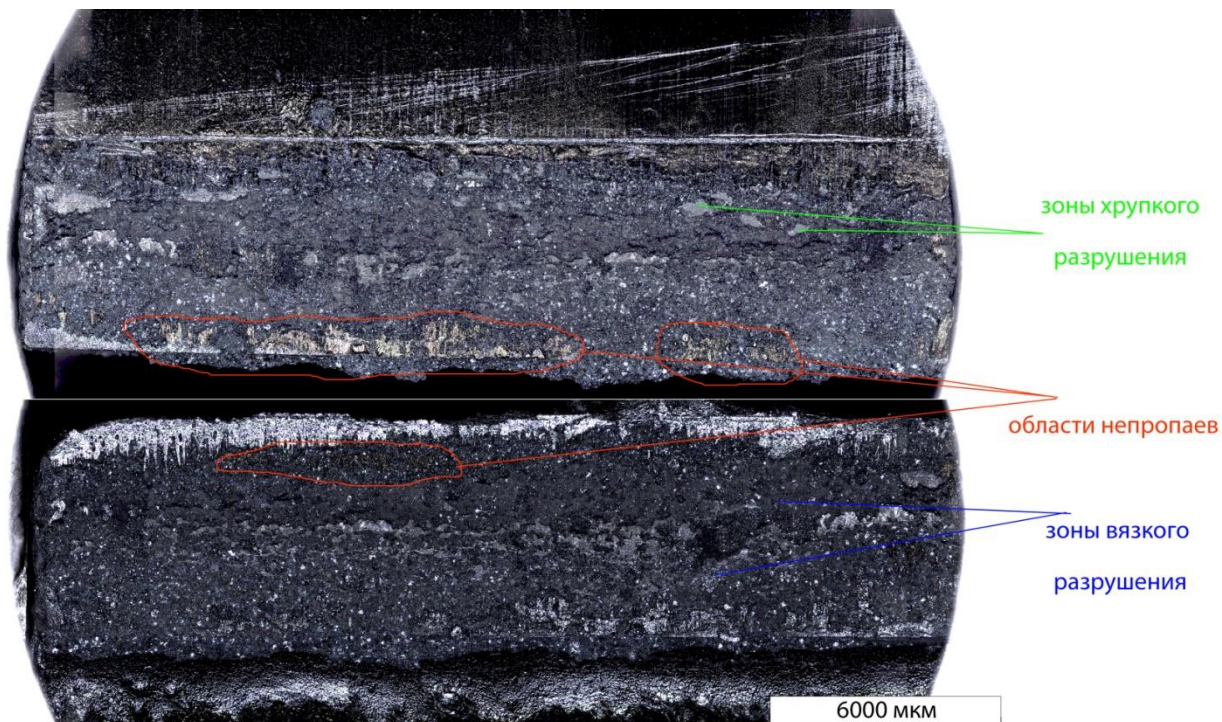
Излом образца №1 первой серии механических испытаний
